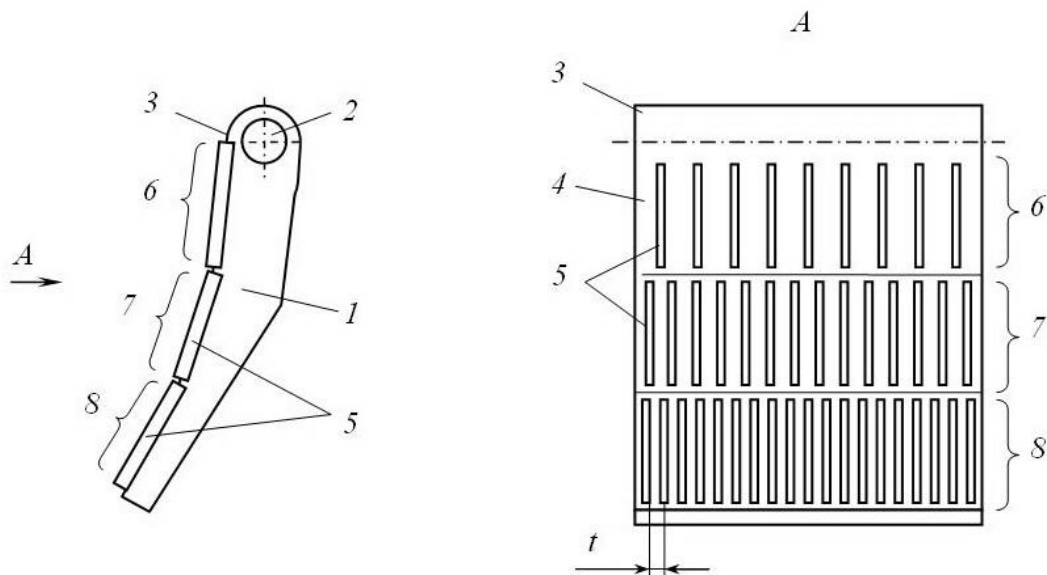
Схема рухомої щоки щоклової дробарки [2]
